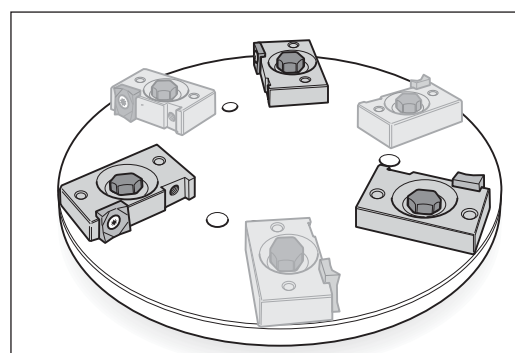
Vous pouvez équiper le plateau de fraisage de 3 et 6 éléments de maintien. Chaque élément doit au moins supporter une plaque réversible.
